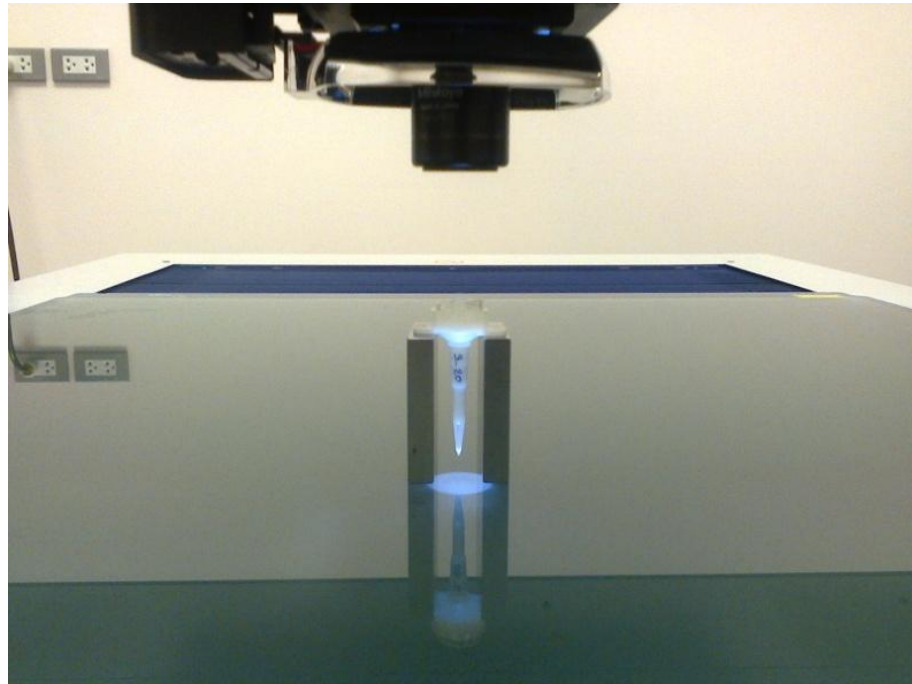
การแสดงผลของเครื่อง CNC Vision Measuring Machine สำหรับ IV Set 20 no.1
